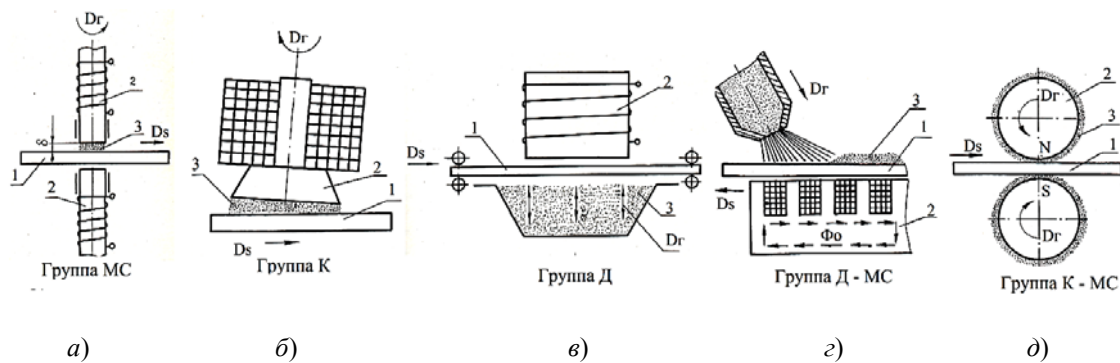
Схемы и устройства магнитно-абразивной обработки плоских поверхностей по виду взаимодействия инструмента с обрабатываемой поверхностью
